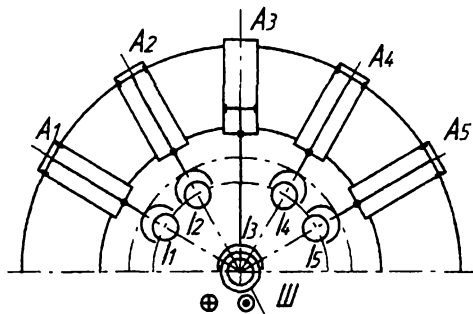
Схема МАЗІ з автооператором на кожний інструмент
